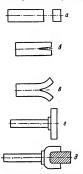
Эскизы переходов пря ковке вилки шариирной передачи сенокосилки:
